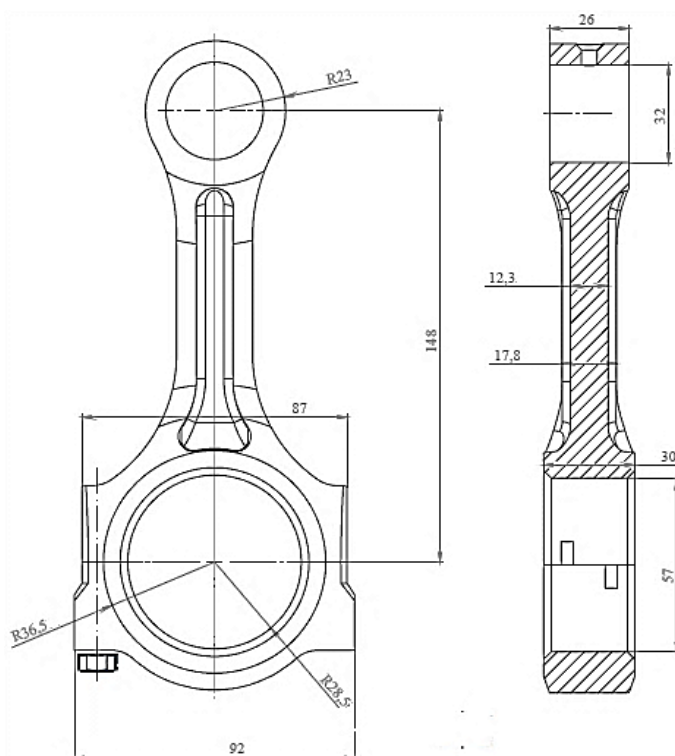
Шатун трехцилиндрового дизельного двигателя
